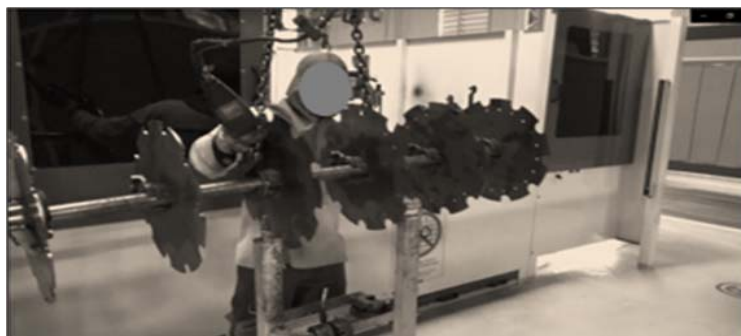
PEÇAS E DISPOSITIVO DE SOLDAGEM
